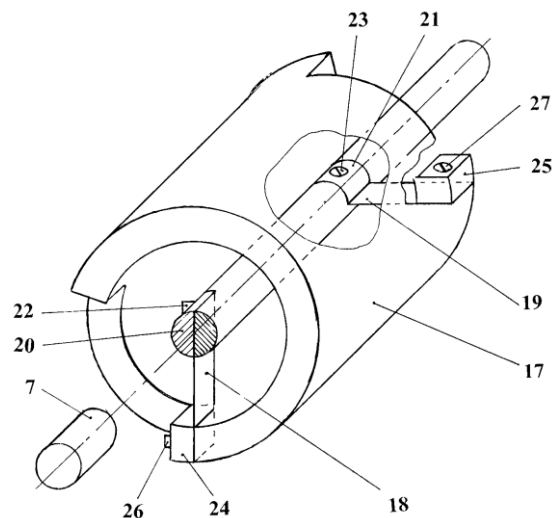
Кинематическая схема подшипника качающегося рычага
